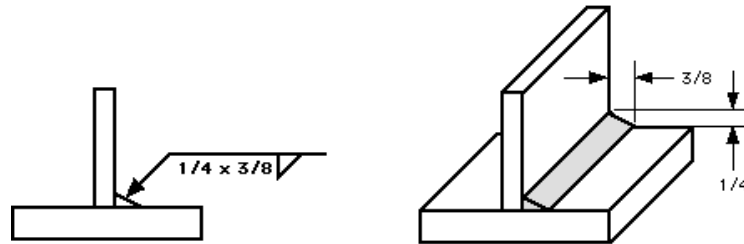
Soldadura de filete (Caras desiguales)¹²
